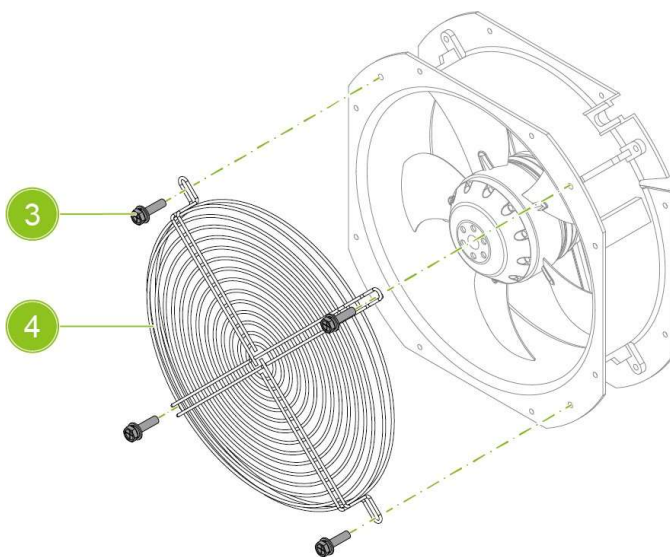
Orifícios de fixação da placa de montagem do ventilador de resfriamento
